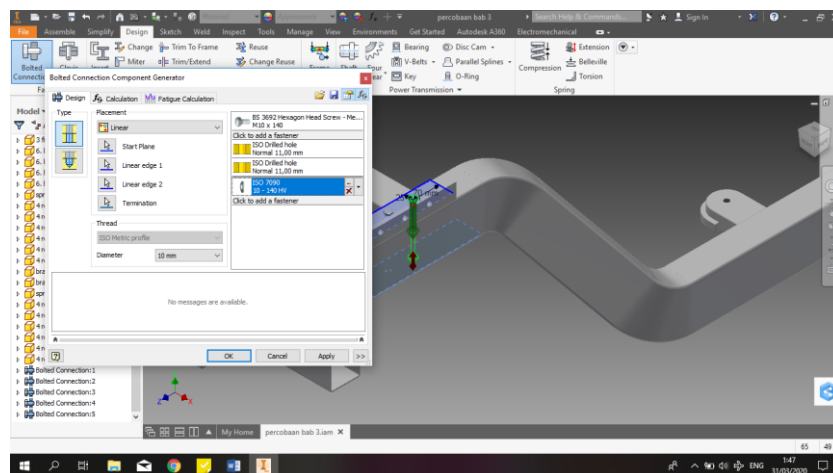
Tampilan Proses *Assembly* pada *Tab Assemble
